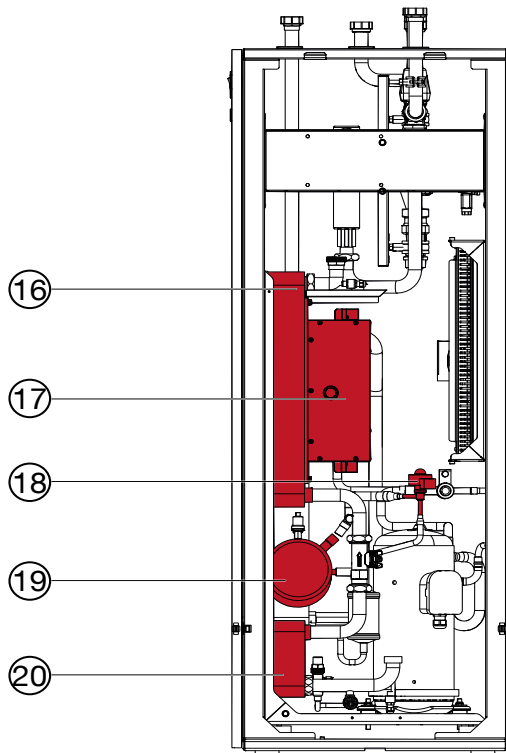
Wärmepumpe Seitenansicht geöffnet
